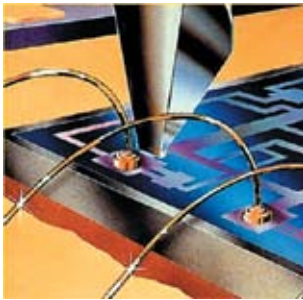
Пример сварки сложного изделия, выполненной на установке 56XX
